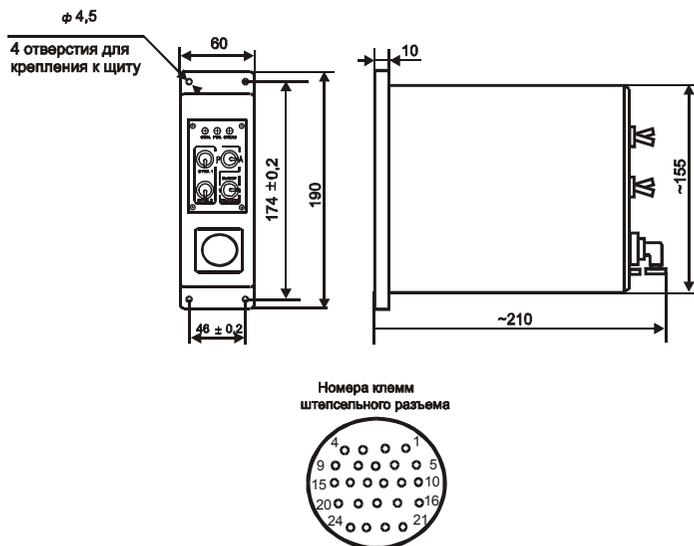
Габаритные и установочные размеры блока БУН-02М
